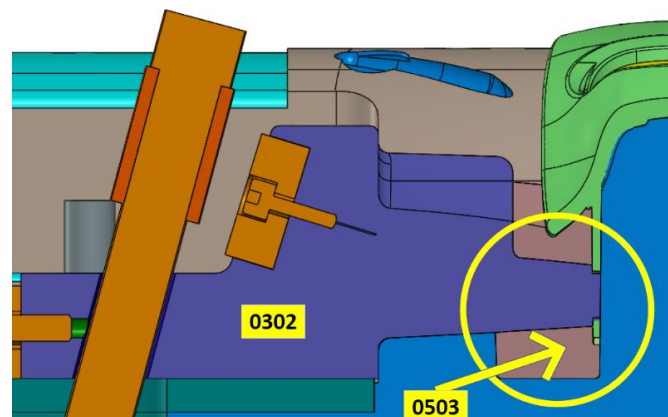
Pormenor da execução da gravação na peça dos movimentos horizontais
